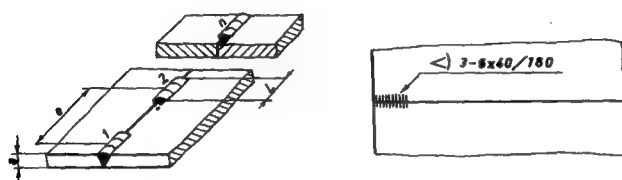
Representaciones unificadas de soldadura única interrumpida, sobre chapa de espesor $a = 3$ mm, con $n = 6$ segmentos de longitud $L = 40$ mm y paso $e = 160$ mm.
